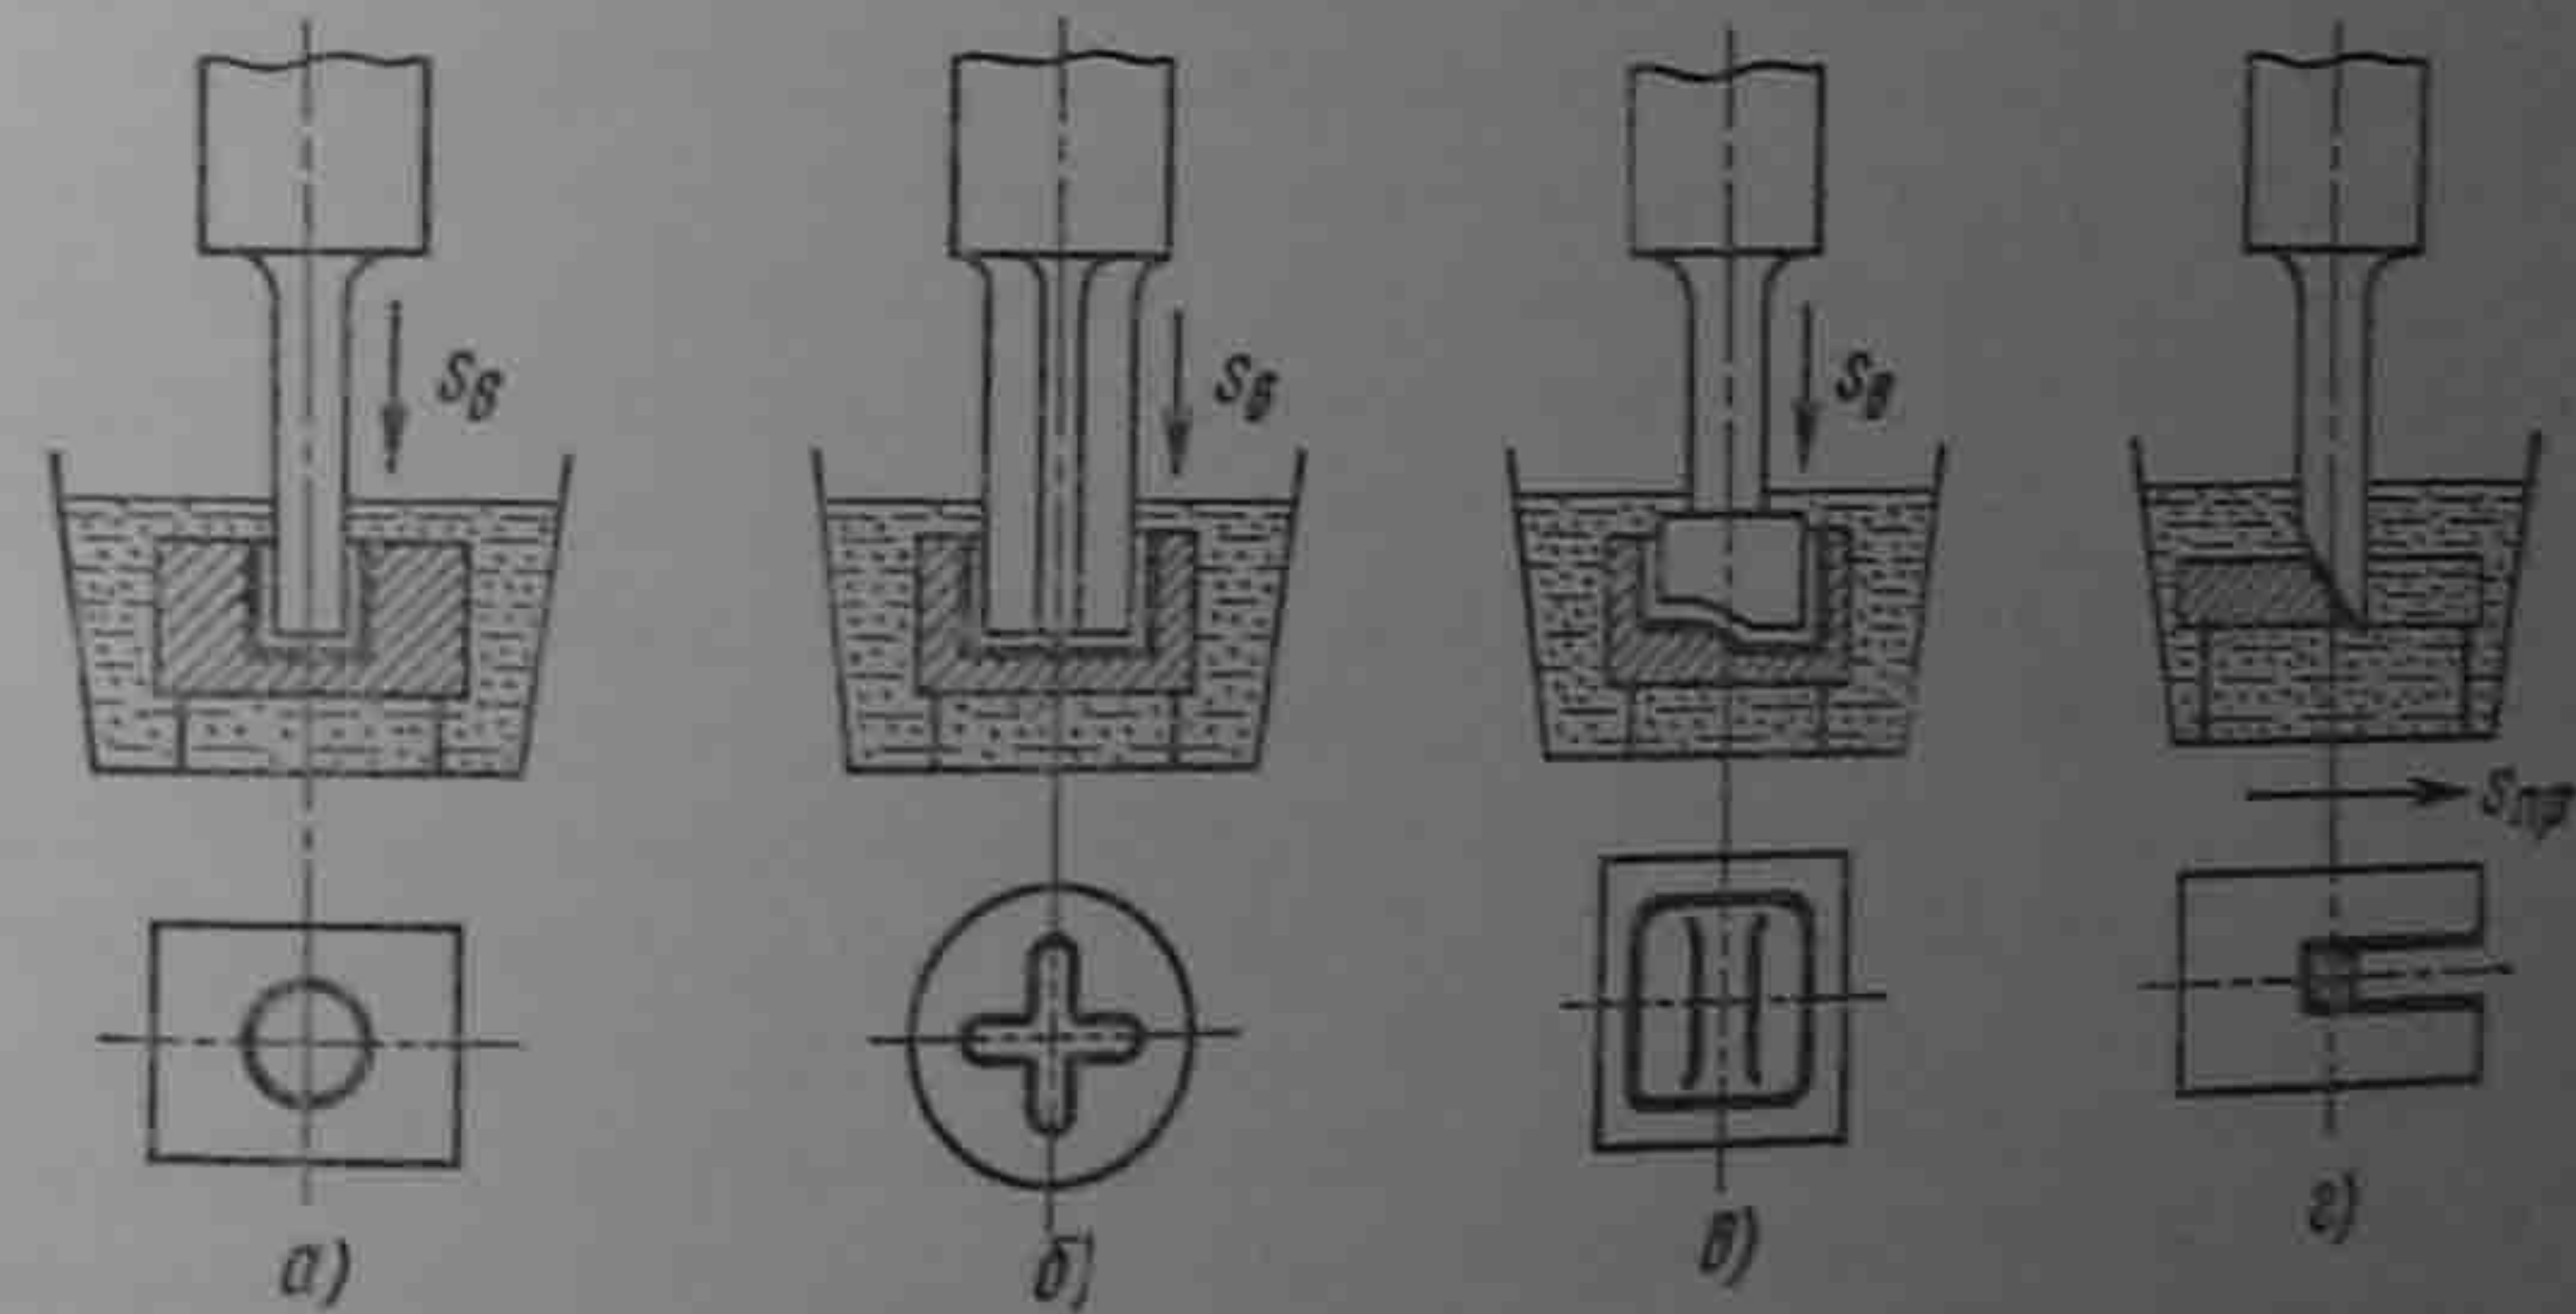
Схемы ультразвуковой обработки поверхностей заготовок: а и б — прошивание цилиндрического и фасонного отверстий; в — обработка внутренней полости; г — разрезание
